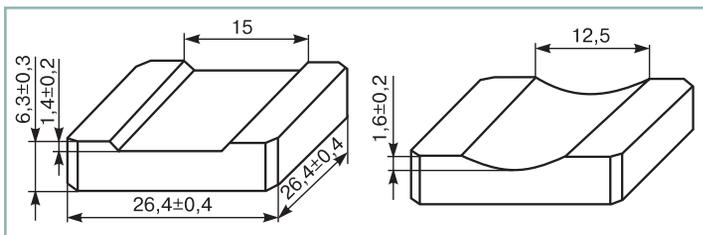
Керамические подкладки: а — КП-АН-061 (для ручной дуговой сварки); б — КП-АН-062 (для механизированной сварки в защитных газах)
